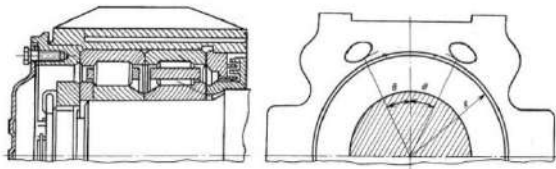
Буксовий вузол з прорізами у верхньому зводі корпусу
